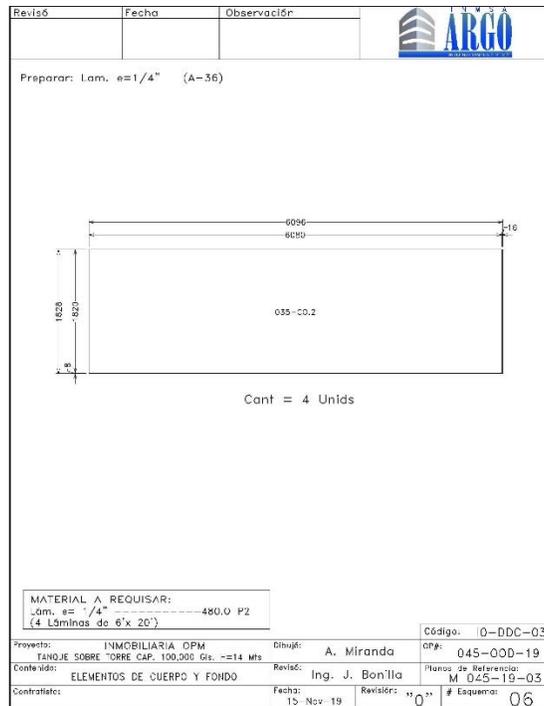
Esquema de corte de elementos de cuerpo, tanque cap. 100 Gls.
